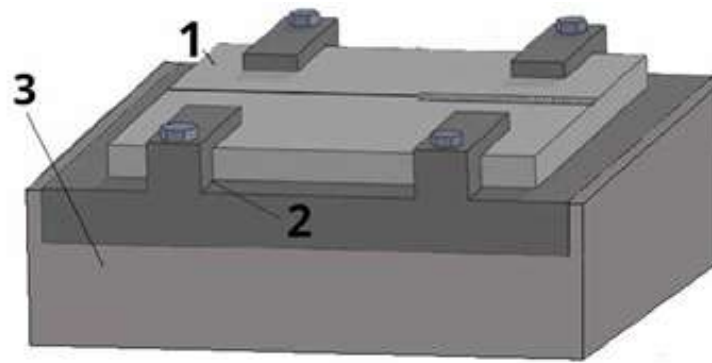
Конструктивна схема пристрою для попереднього підігріву зразків: 1-зразок для зварювання; 2-прижимні кронштейни; 3-піч з нагрівальною спіраллю
